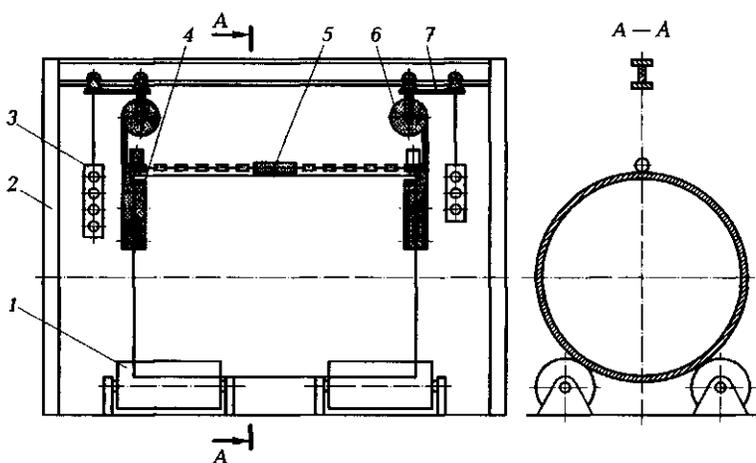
Установка для сборки продольных стыков обечаек:
